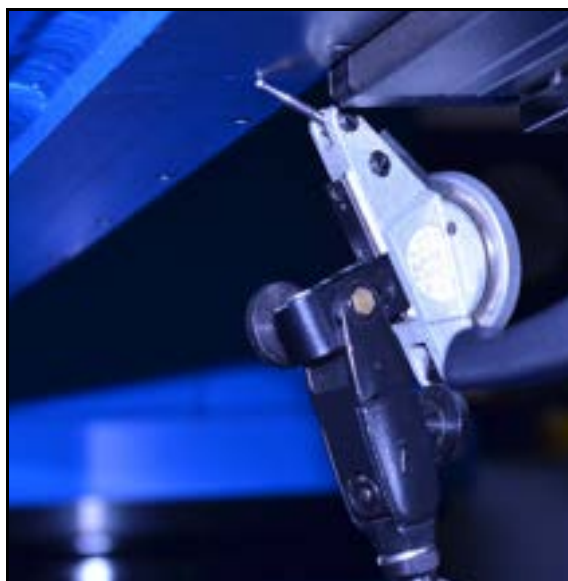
INDICATEUR TOUCHANT LA SURFACE DU COULISSEAU DE LA MACHINE
